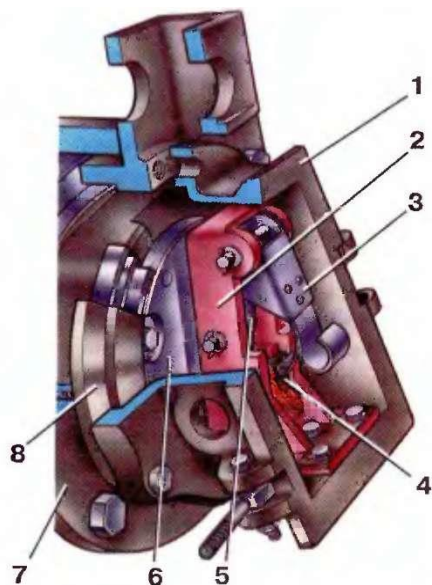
Заземлюючі пристрої букси моторного вагона: 1 – корпус; 2 – щіткотримач; 3 – важільний пристрій; 4 – щітка; 5 – пружина; 6 – струмознімальна кришка; 7 – букса; 8 – лабіринтова кришка
